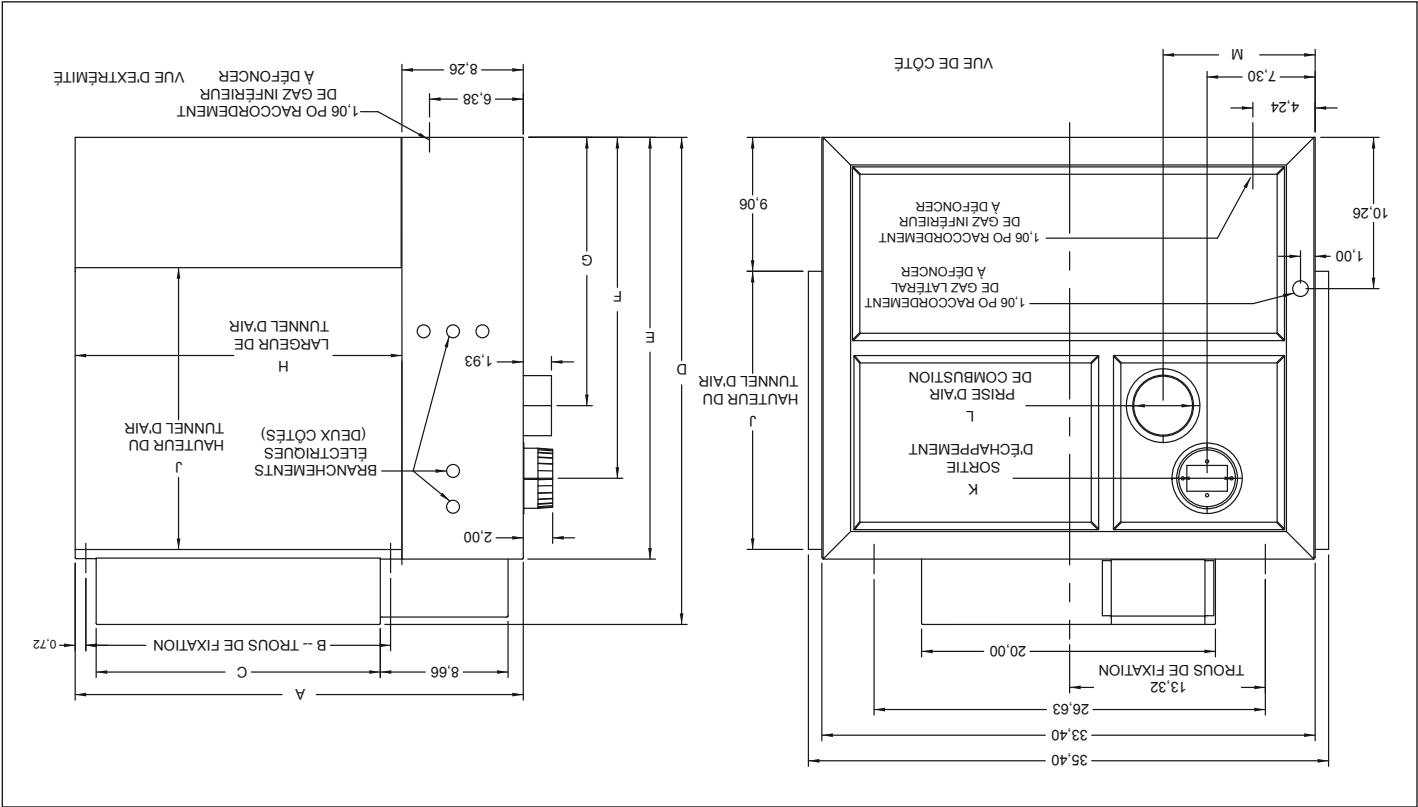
Dimensions de la chaudière canalisée d'intérieur à combustion séparée (toutes dimensions en pouces)
